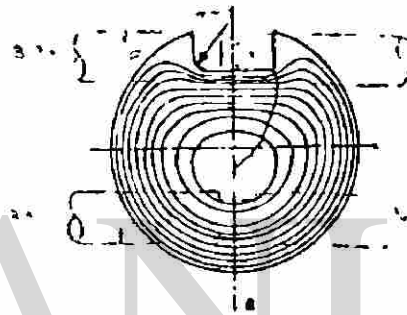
Sección de rotura por fatiga de un eje con chavetero. La grieta se inicia en el ángulo no redondeado.
